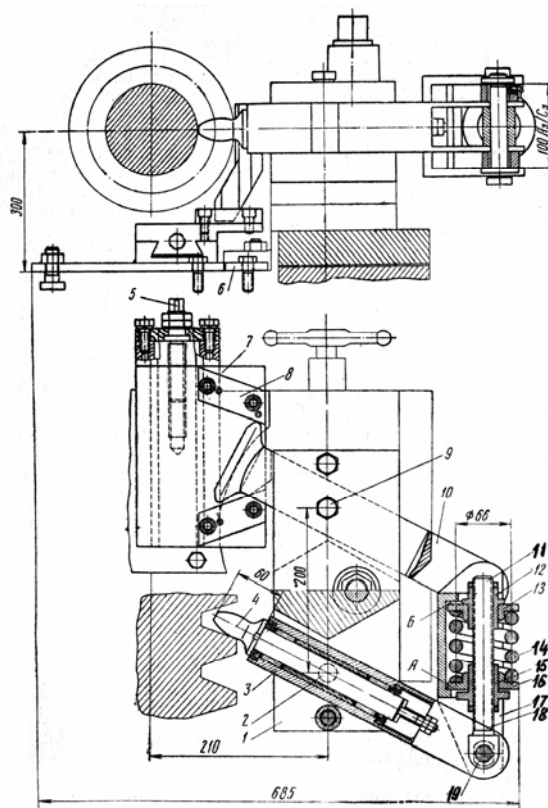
Однороликовое устройство для обкатывания огибанием резьб и червяков с шагом более 16 мм
